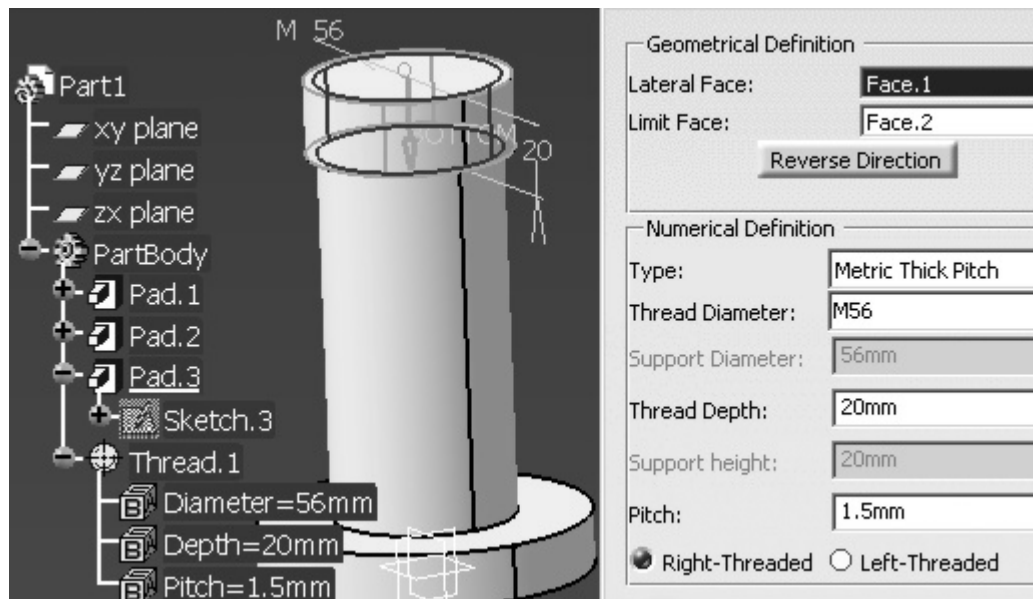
Executarea filetului de prindere pe capătul corpului robinetului
